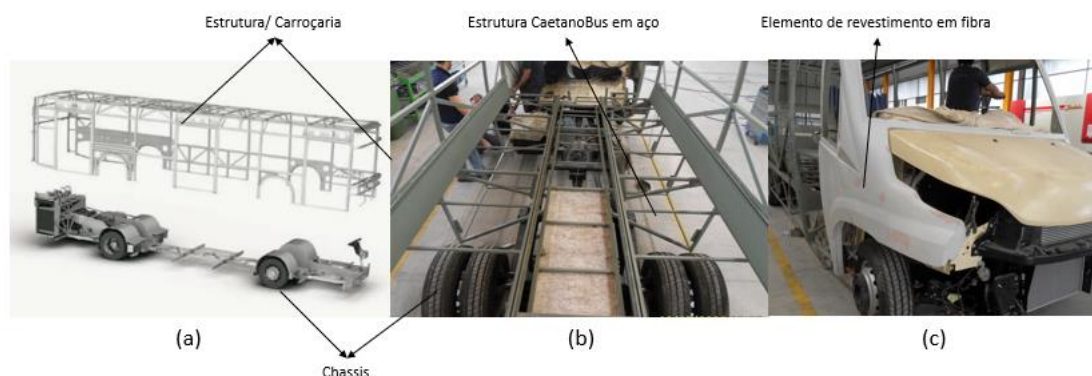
(a) Vista explodida de estrutura semi-integral [18] (b) Estrutura em aço CaetanoBus (c) Elemento de revestimento
